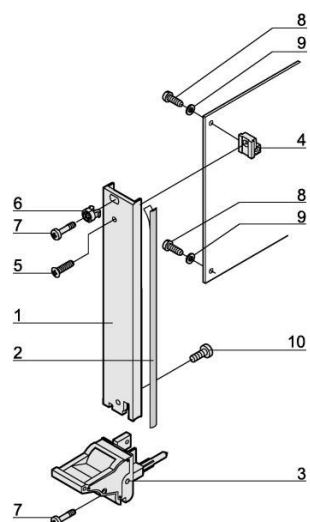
Muntatge de la pinça al panell i subjecció del panell al PCB.
